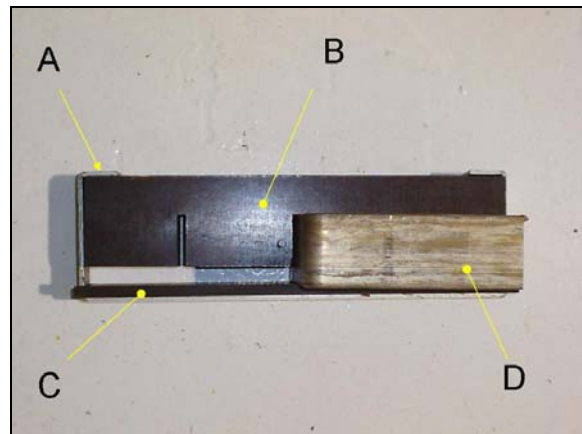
A) Support en acier B) Bloc isolant en bakélite à l'horizontale avec trois encoches C) Pièce isolante en bakélite verticale plate de 6 mm D) Barre omnibus dans l'encoche centrale
